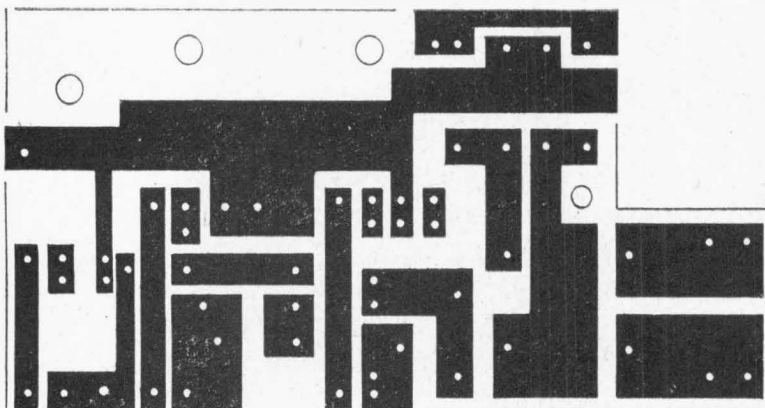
Vista da face cobreada da plaqueta de circuito impresso empregada nesta montagem.
